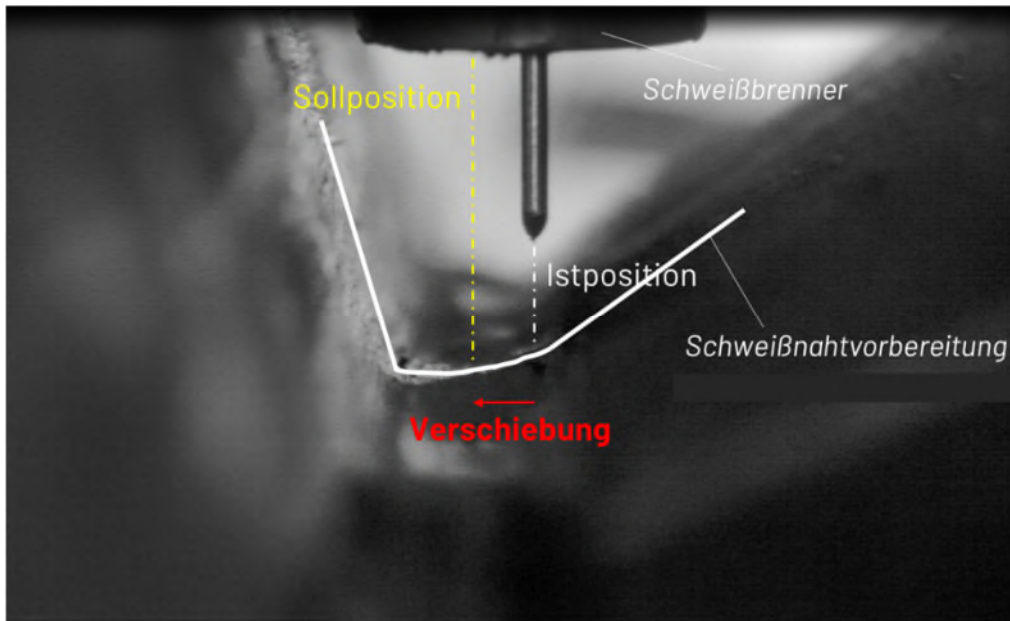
HDR Kamera Livebild als Hilfsmittel bei der korrekten Positionierung des TCP (Schweißdrahtposition) in der Schweißfuge
